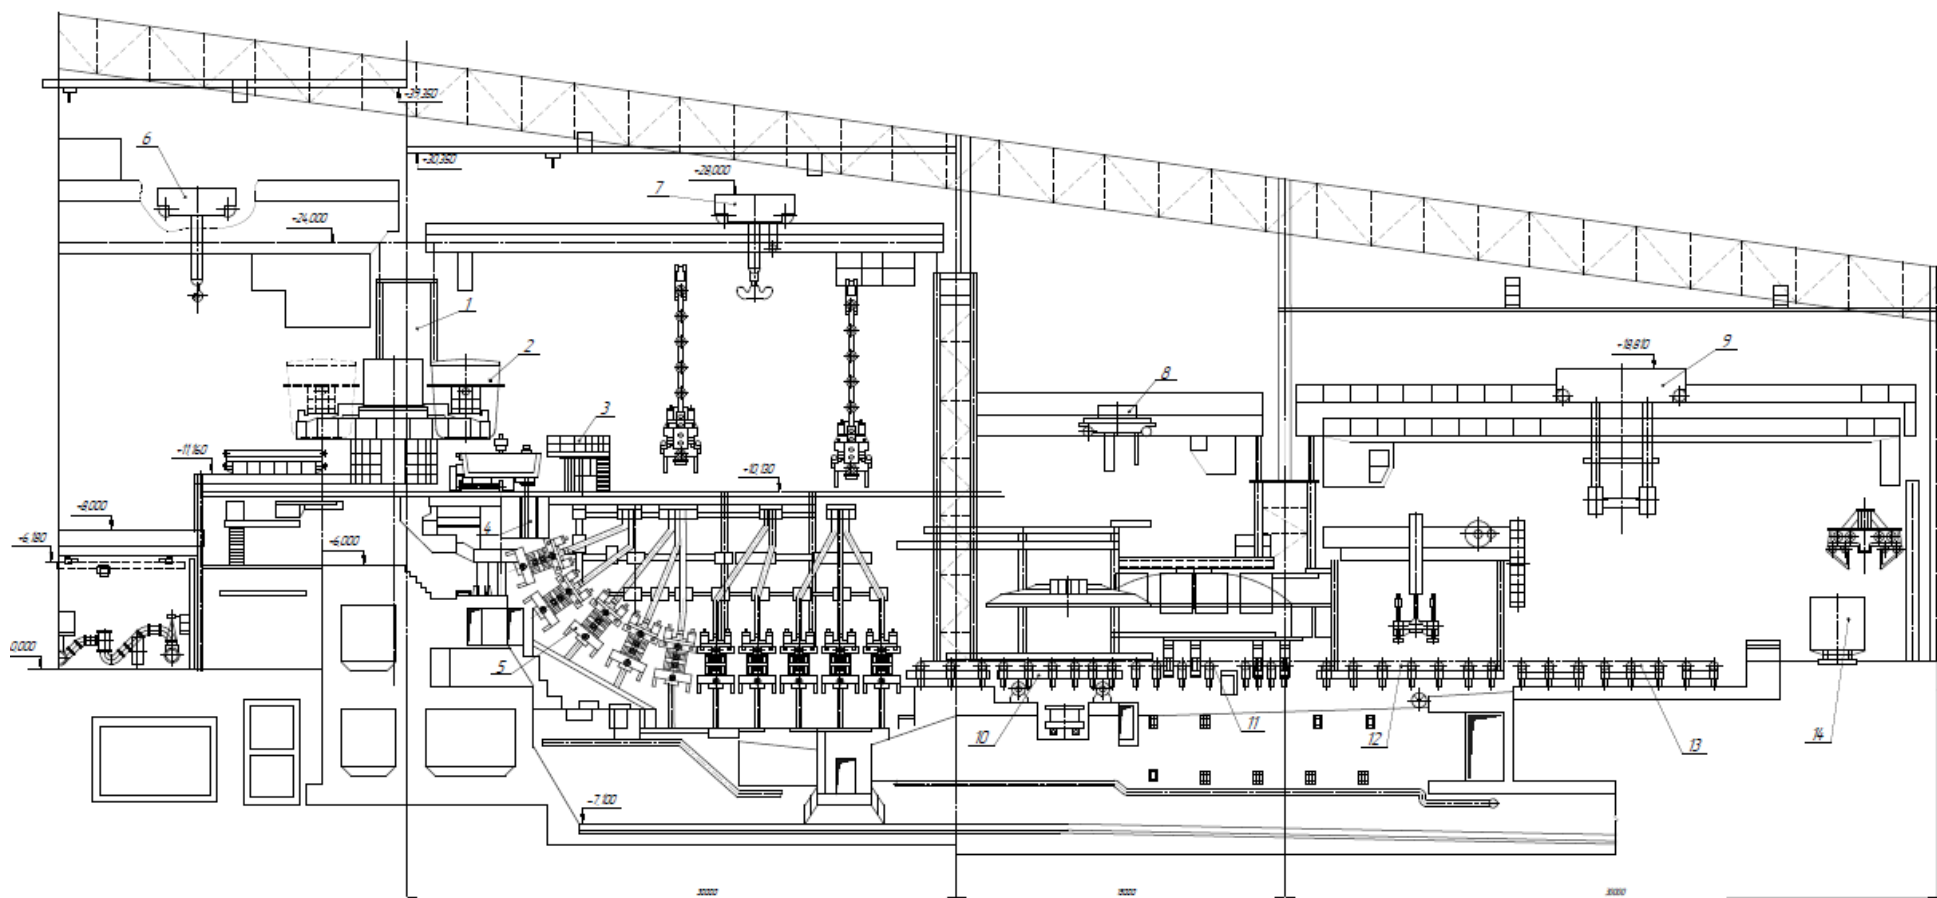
схема МНЛЗ №2. 1 - ППС; 2 - Стальковш; 3 - Балкон; 4 - Кристаллизатор; 5 - Сегменты; 6 - Разливочный кран; 7 - Ремонтный кран; 8 - Вспомогательный кран; 9 - Кран уборки сляб; 10 - Падающие ролики; 11 - Агрегат порезки на мерные длины; 12 - Транспортные рольганги; 13 - Стол разгрузки; 14 - Вагоны [9]
